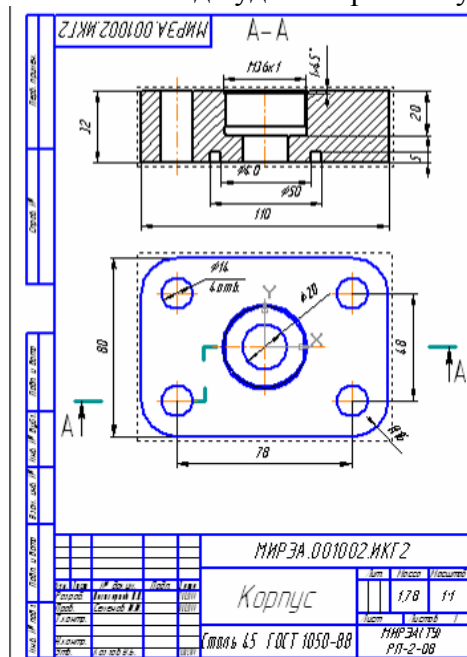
Ассоциативный чертёж Корпуса
